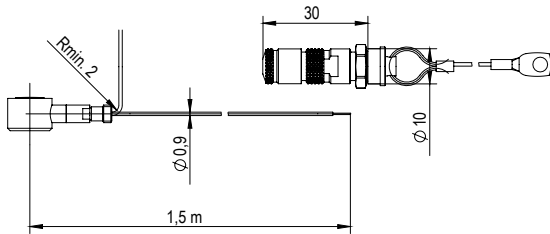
Kraftsensor Typ 9204BE mit Kabel und Stecker
